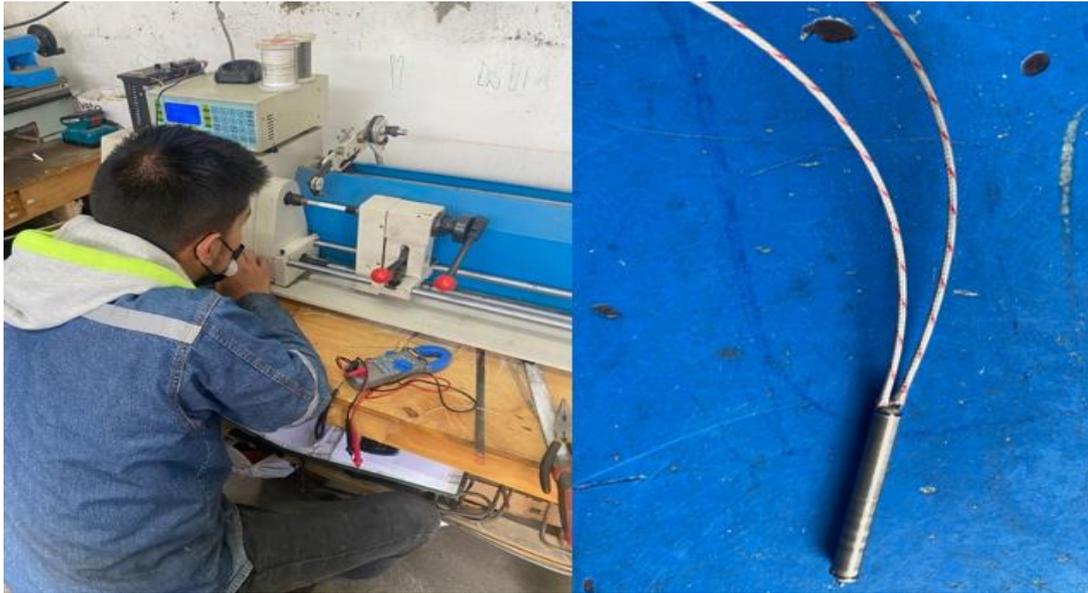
Proceso de rebobinado: a) Operario con la máquina bobinadora; b) Varilla de cerámica bobinada con terminales
